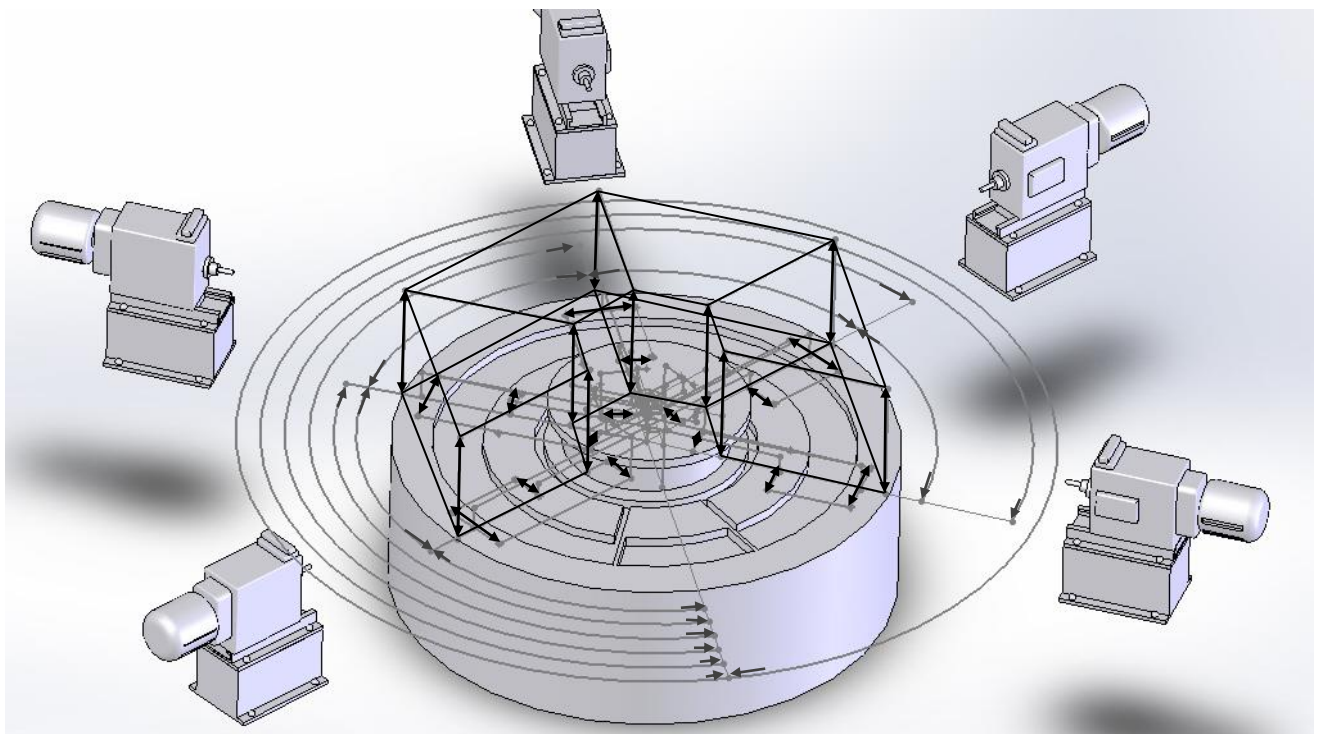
Розмітка станини під монтаж силових агрегатів і пристосувань нової компоновки агрегатного верстата
